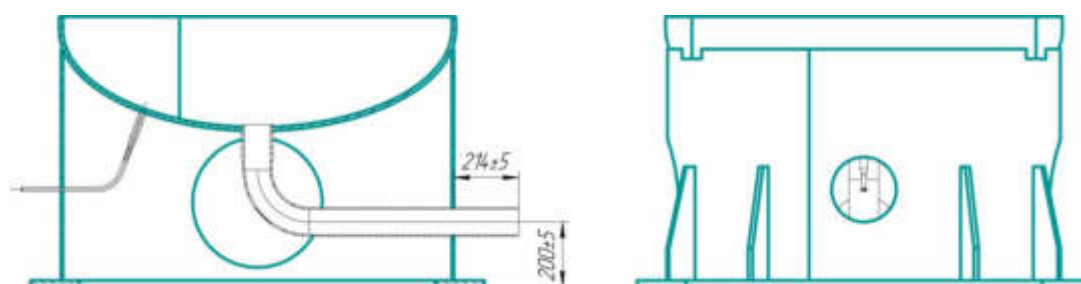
Схема сборки днища нижнего и обечайки опорной
